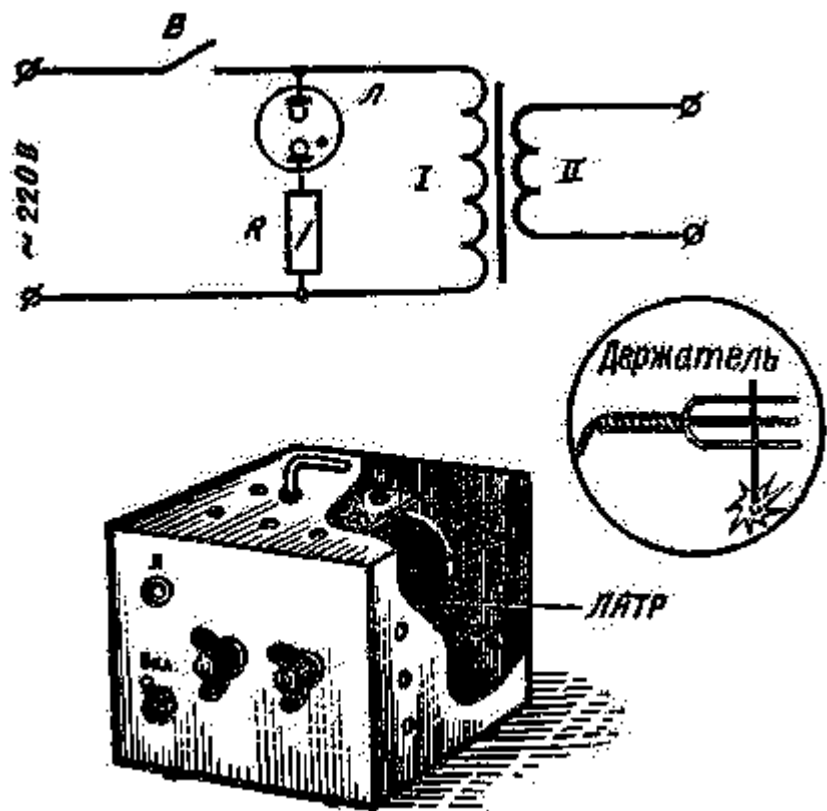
Портативный сварочный аппарат (первая конструкция)
